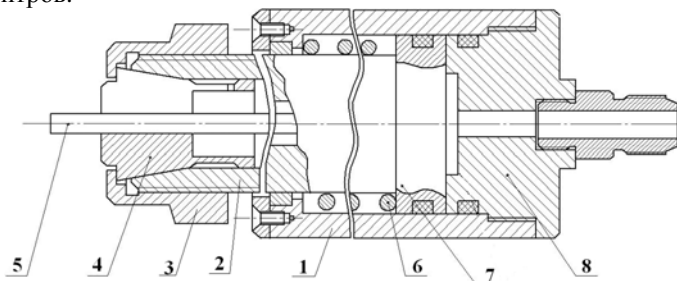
Приспособление для фрикционного нанесения покрытий.
